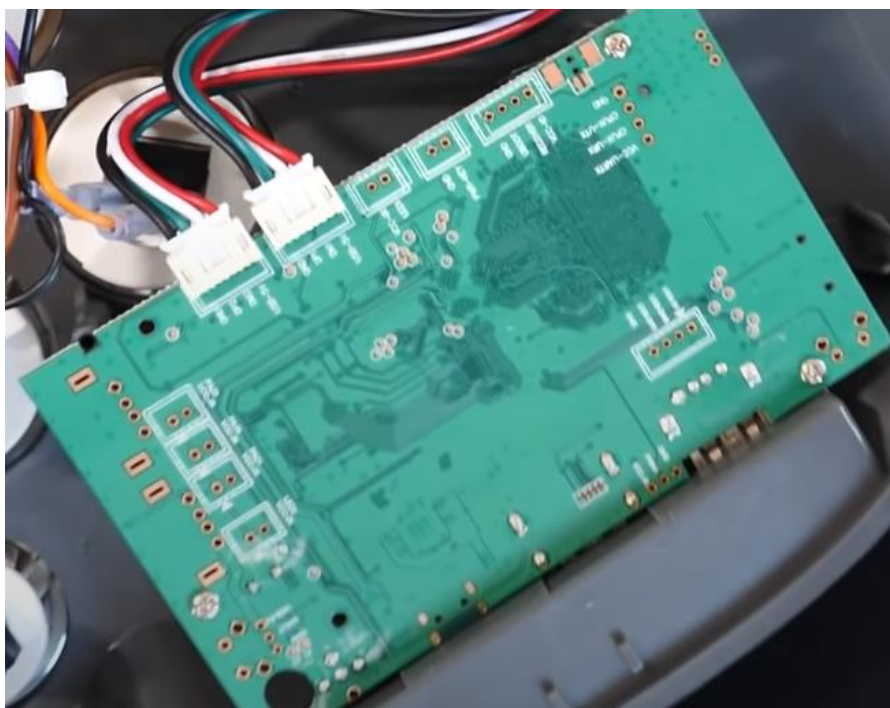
CHA PCB. Fuente de la imagen: <https://youtu.be/FX1IzTYOk8M>
